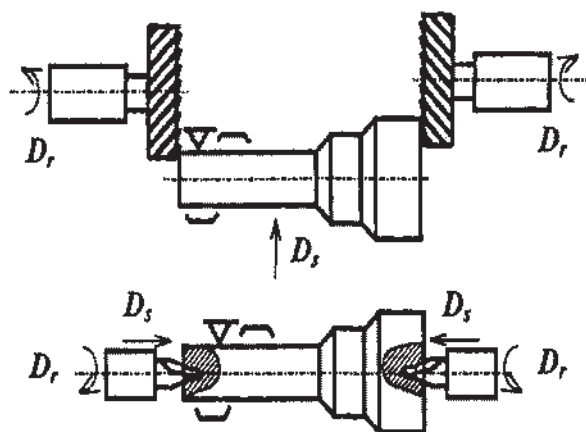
Схема обработки торцов и центровых отверстий на фрезерно-центровальном станке
